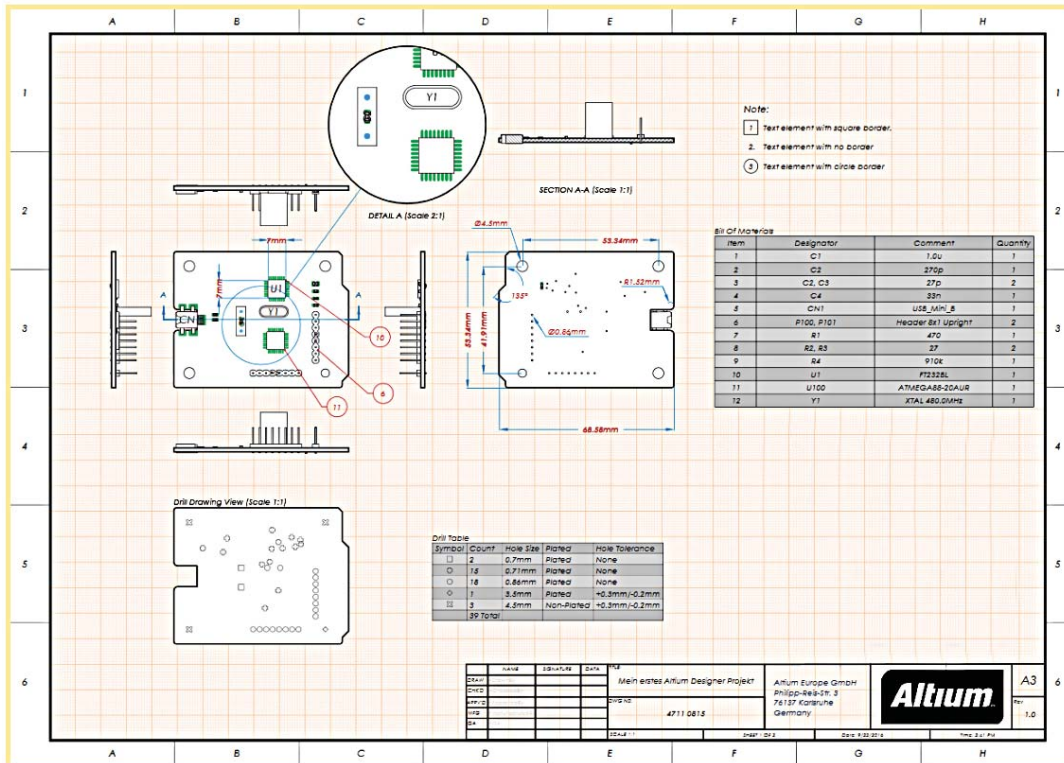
Beispiel einer Zeichnung aus Draftsman (Details für den Bestücker).
